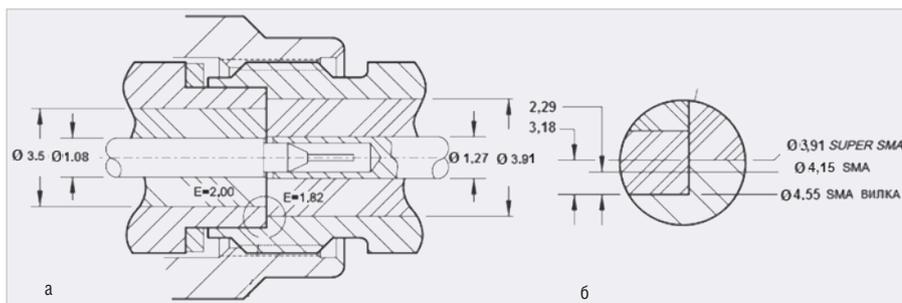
Вилка и розетка соединителя: а) в сочленённом состоянии; б) размеры области контакта вилки и розетки
